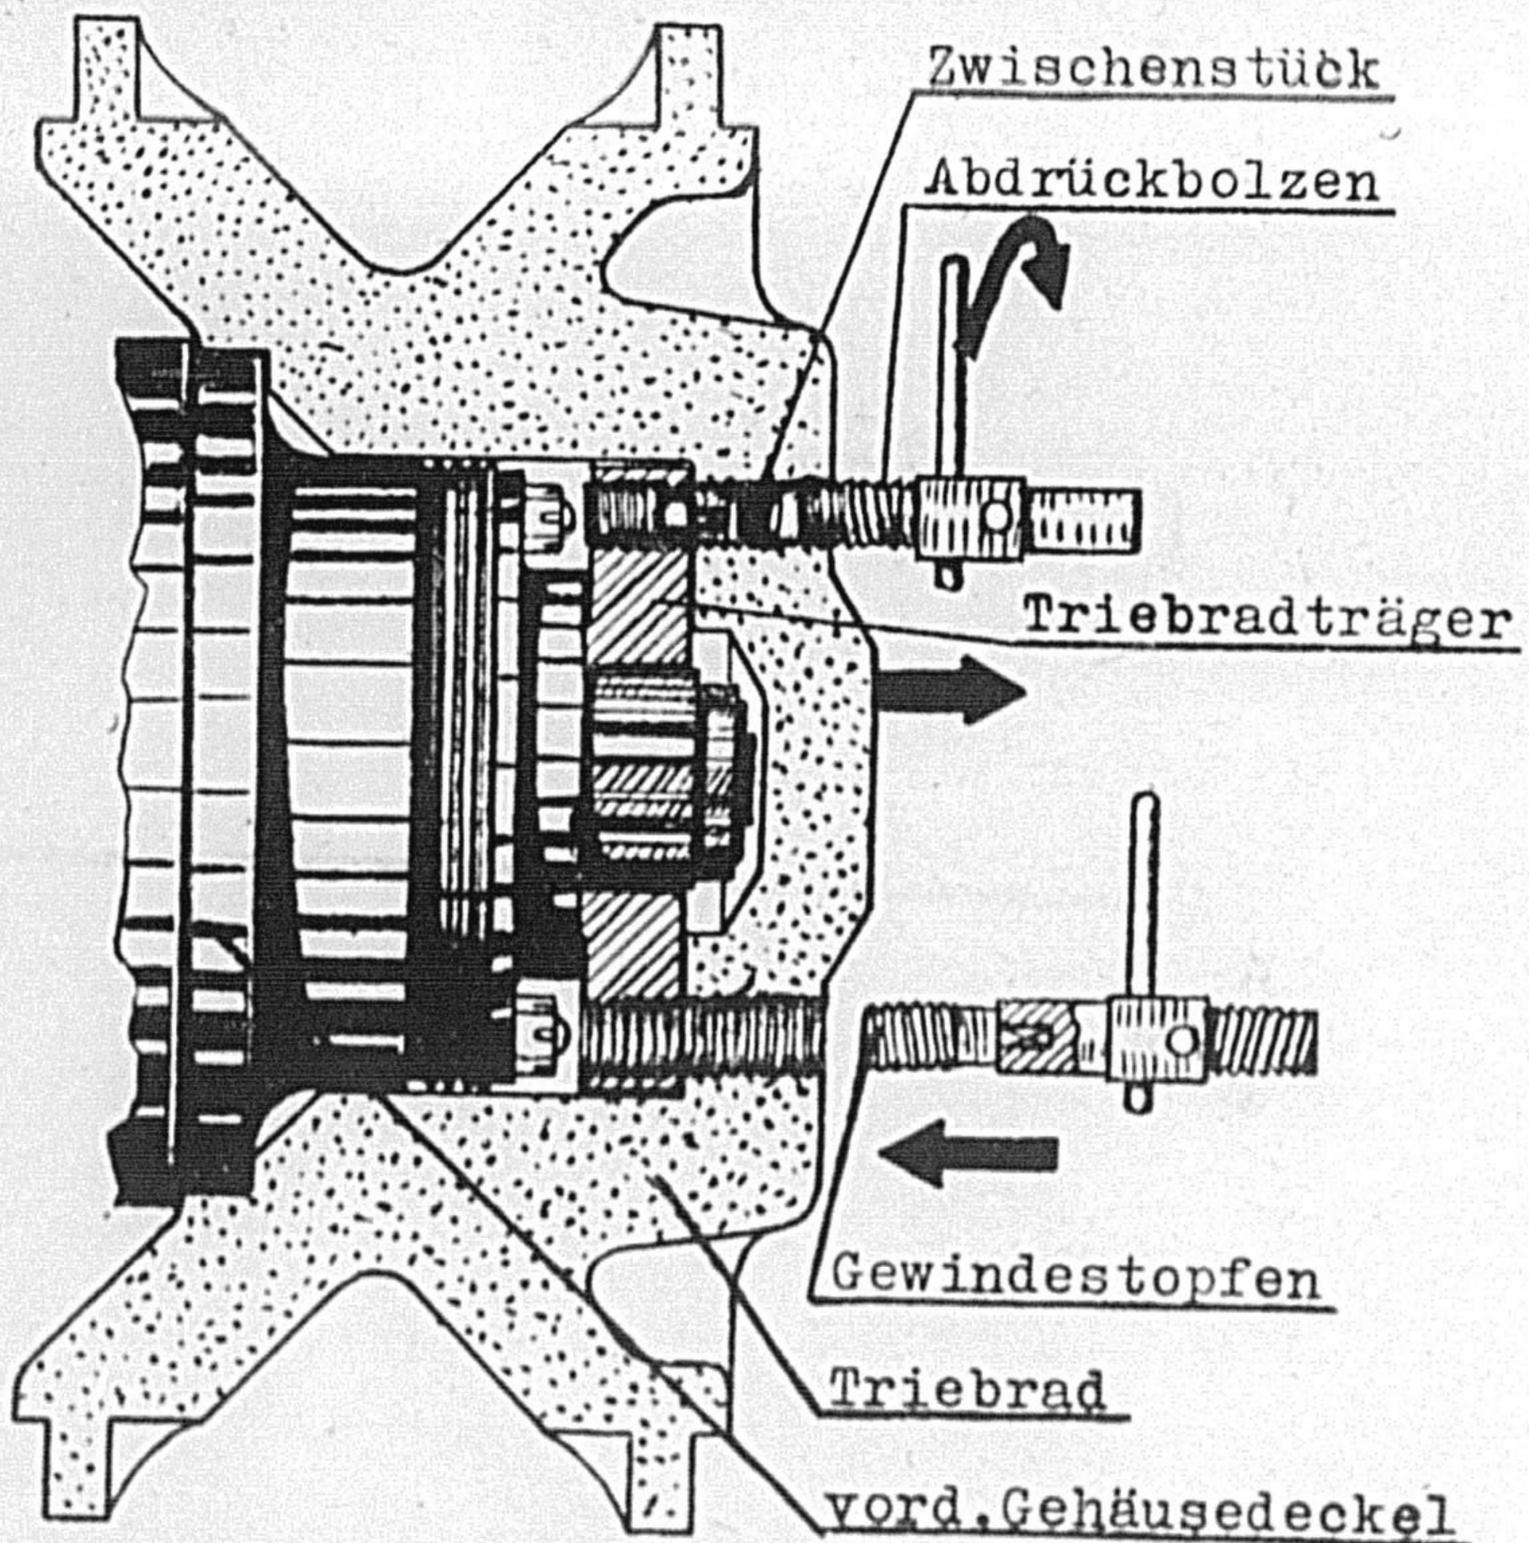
a Einschrauben der Gewindestopfen, Abdrücken des Triebrades
